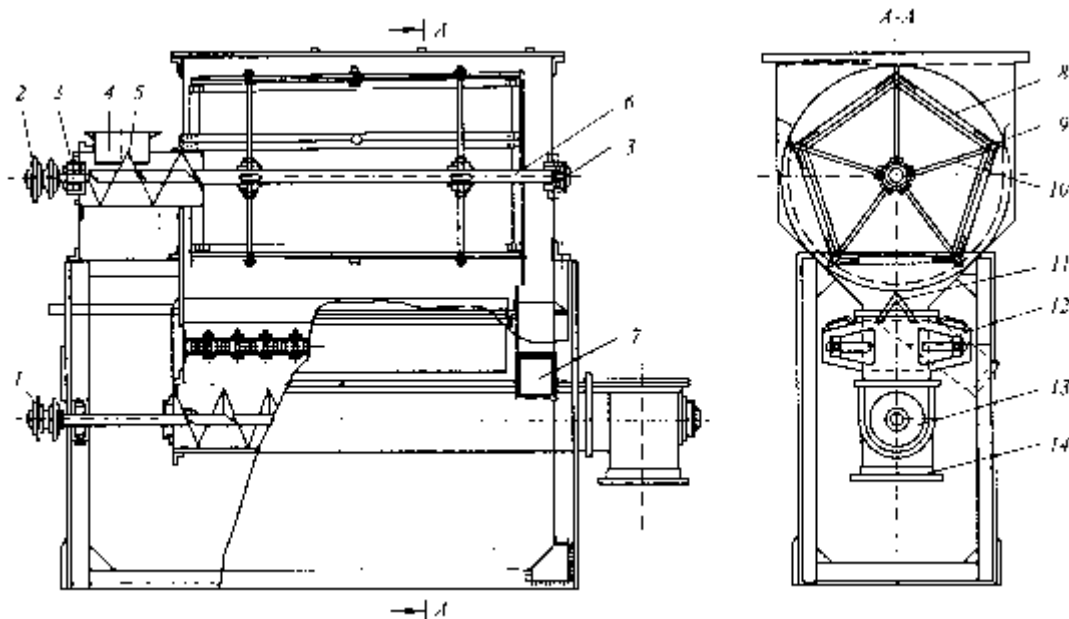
Принципиальная схема просеивателя с барабанными ситами: 1, 2 - звездочки; 3 - подшипник качения; 4 - входное отверстие; 5 - короткий шнек;
